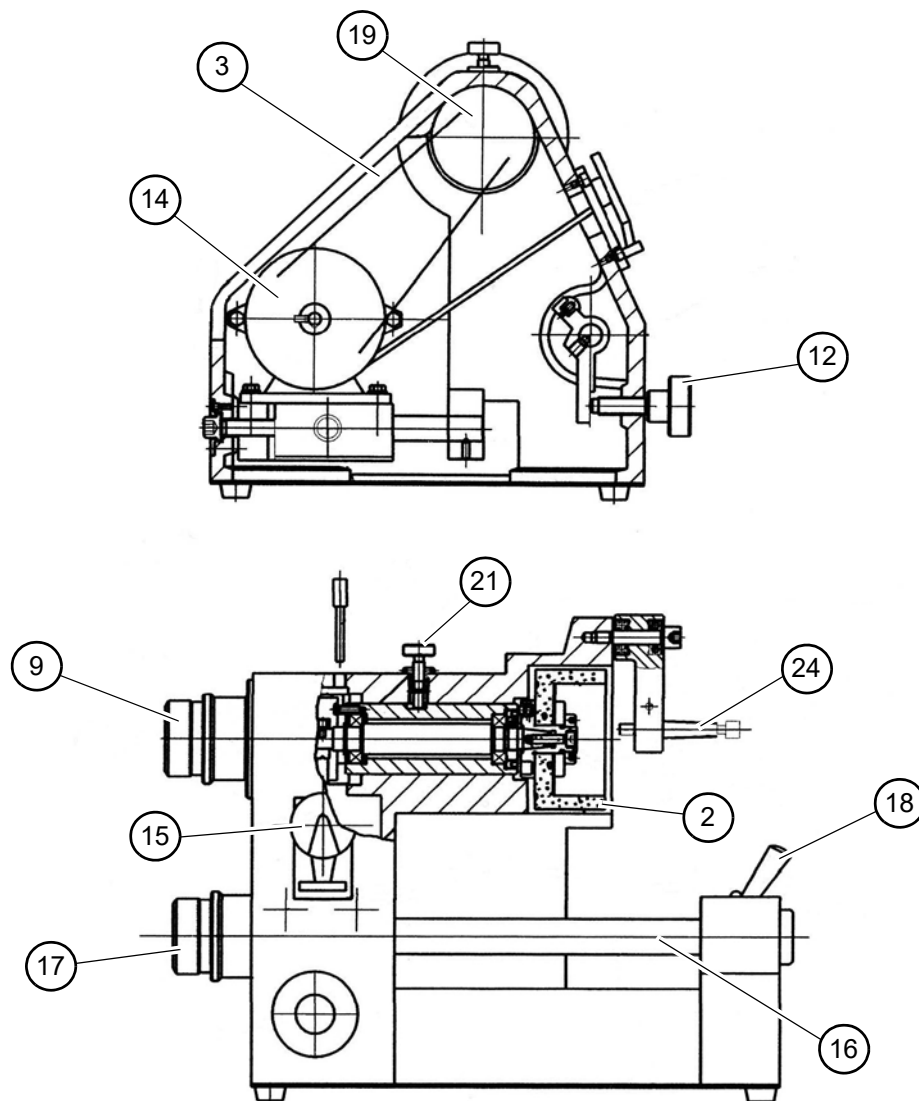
Stichel- und Werkzeugschleifmaschine
